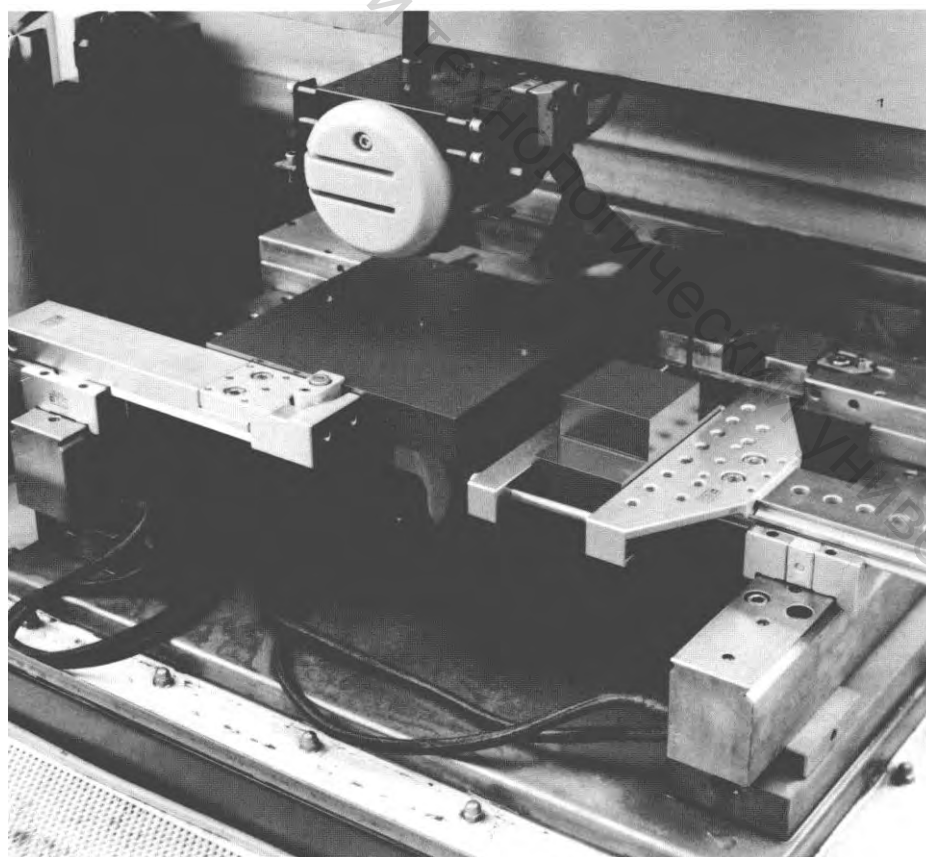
Пример одновременной установки в приспособлении двух заготовок
